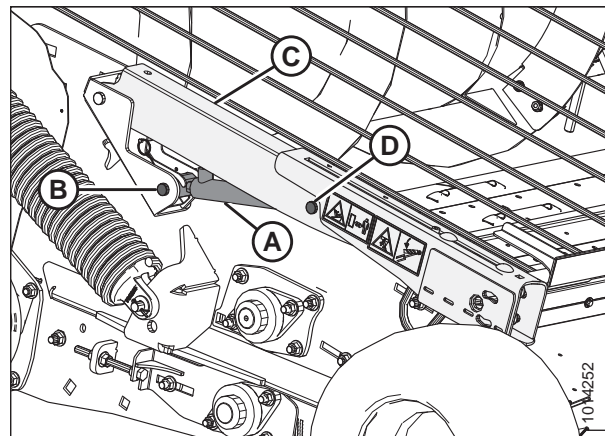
Вспомогательный гидроцилиндр — Правая сторона жатки
